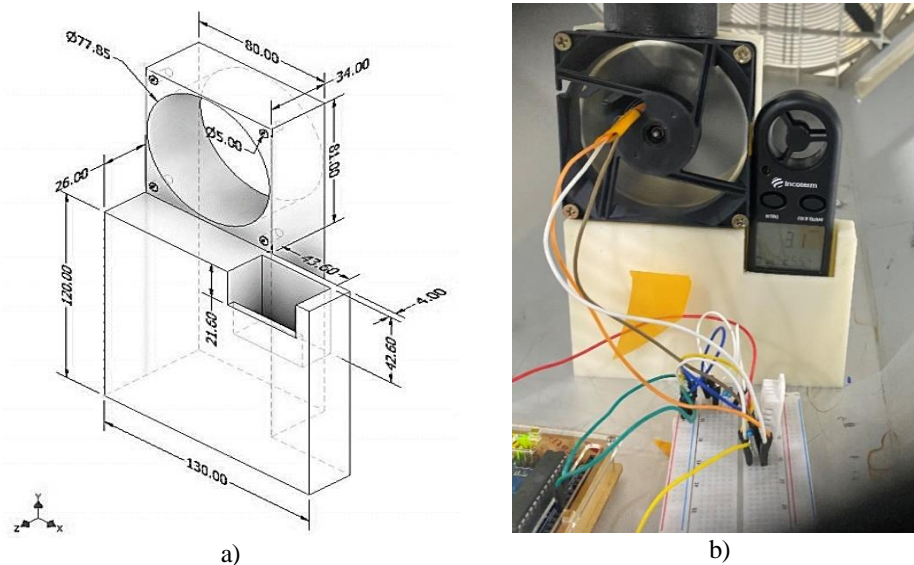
Base para calibração: a) Desenho técnico da base usando o Autodesk Inventor, b) Base impressa com a montagem final (Autores, 2024)
